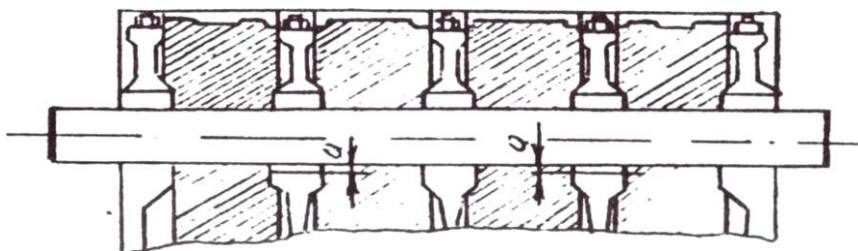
Схема контроля соосности посадочных мест блока цилиндров под вкладыши коренных подшипников с помощью оправки
